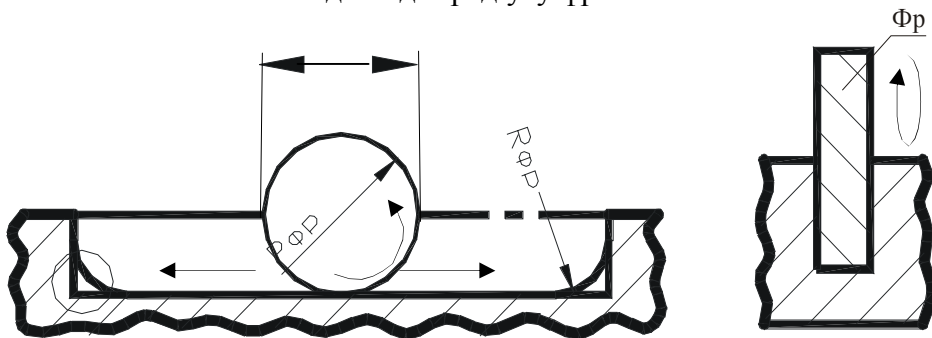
Фрезерування: обробка площини торцевою фрезою, радіус порожнини відповідає радіусу фрези
